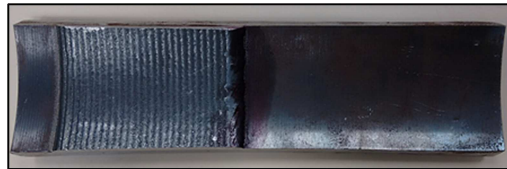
Peça revestida pelo processo de soldagem PTA com pó de Inconel 625, Nistelle 625.
